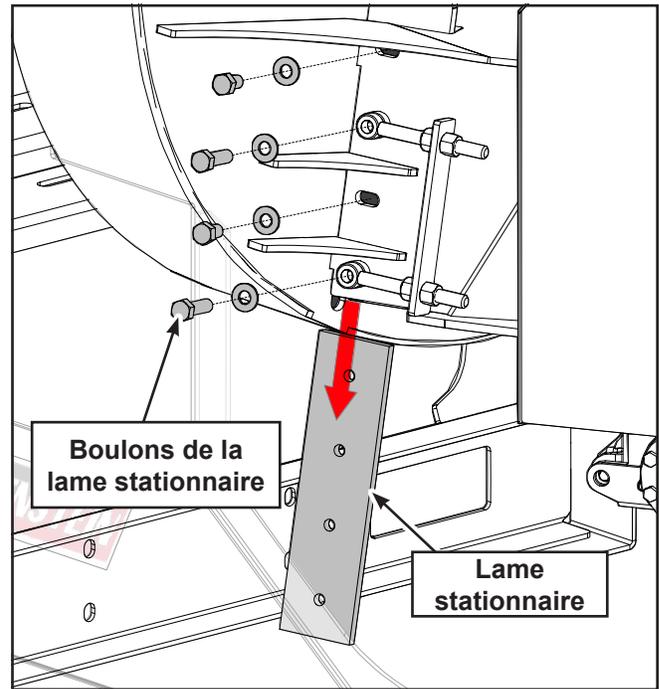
Coupe schématique illustrant l'assemblage de la lame stationnaire
